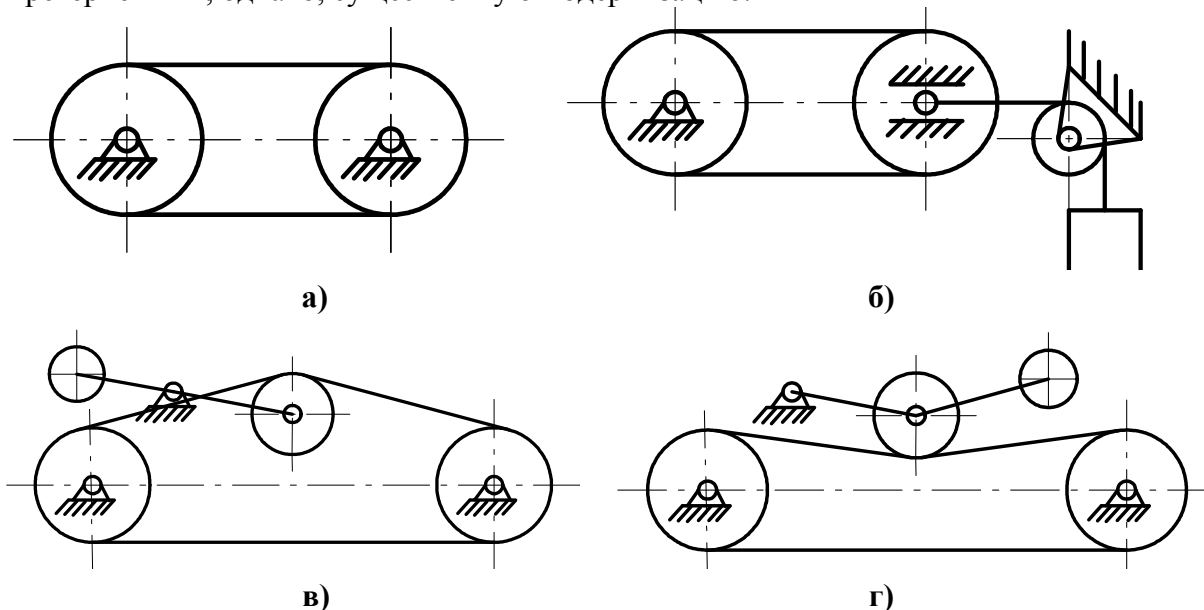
Схемы передач с различными способами натяжения ремня: а - с натяжением ремня за счет его упругости (передача с закрепленными валами); б - с автоматическим натяжением ремня с помощью груза и подвижного вала (передача с подвижным валом); в - с автоматическим натяжением подвижным роликом, установленным на ведомой ветви ремня внутри контура ремня; г - с автоматическим натяжением подвижным роликом, установленным на ведомой ветви ремня вне контура ремня
